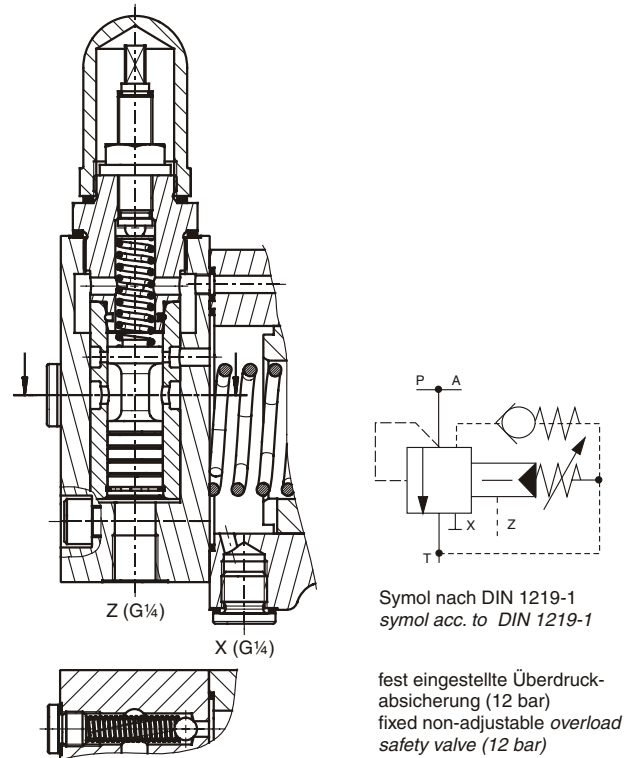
Druckregelventil mit externer Ansteuerung am Anschl. Z
